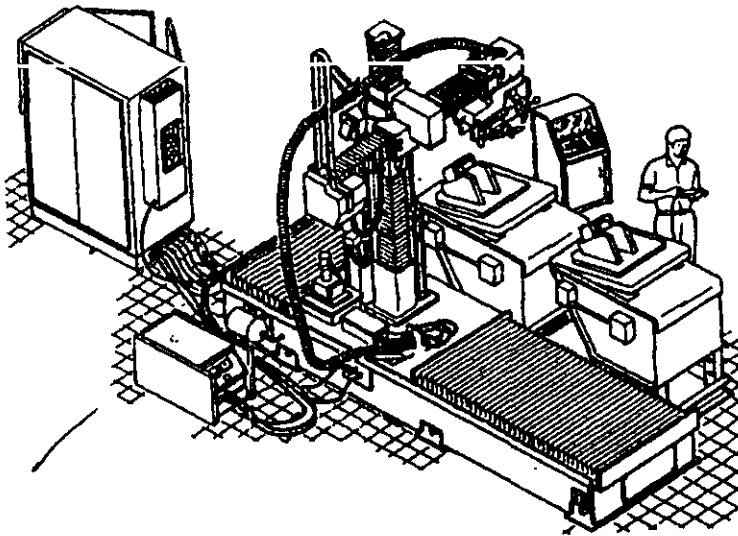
Célula de soldadura por arco con robot³.
